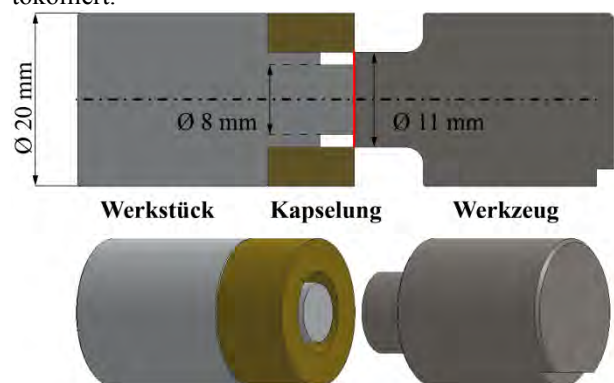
Probenkörper für das Druck-Torsions-Tribometer in Schnittansicht (mit rot markierter Kontaktzone) und als 3D-Modell [13]
